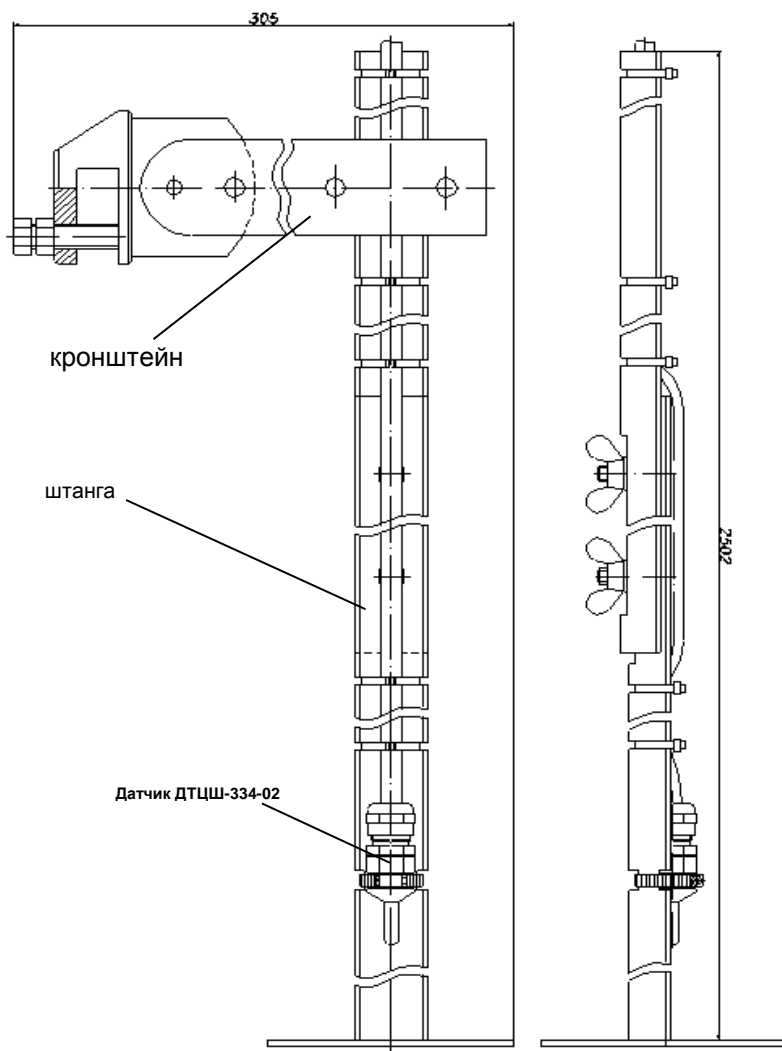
ДТЦШ-334-02 (общий вид)
